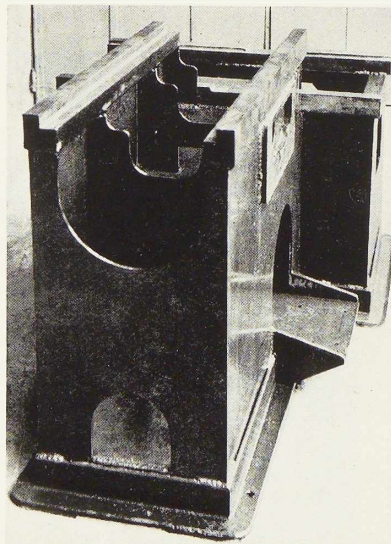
Caisson de soudeuse en acier découpé à la coupeuse automatique et soudé (Electricité et Electromécanique).
